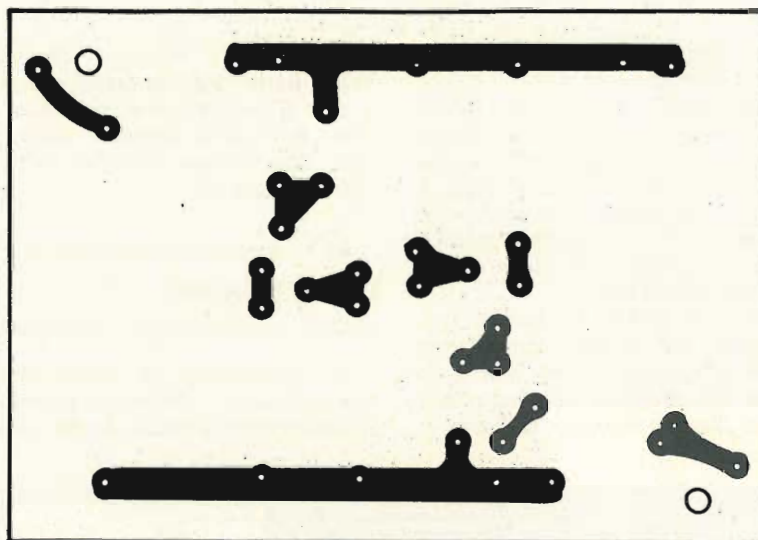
Lato dei collegamenti in rame del semplice circuito stampato su cui viene montato il dispositivo.
